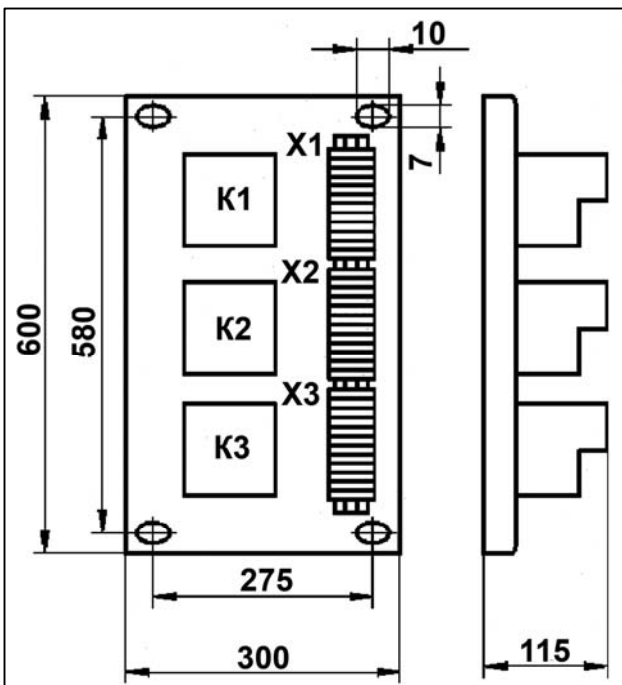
Габаритные и установочные размеры блока БРВ-3-1-У3
